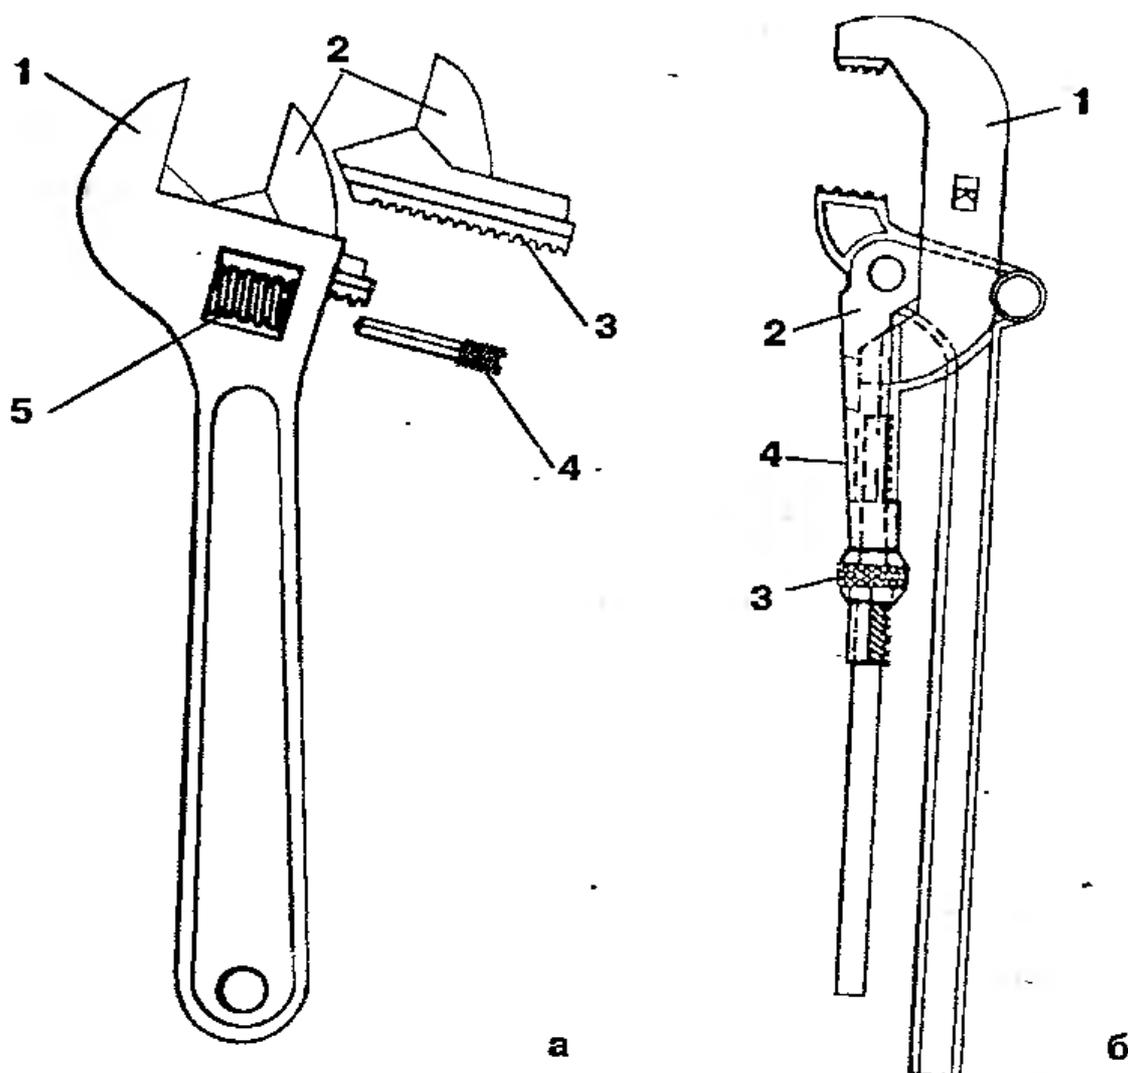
Ключи: а — разводной гаечный (1 — неподвижная губка; 2 — подвижная губка; 3 — рейка; 4 — ось; 5 — червяк); б — трубный рычажный (1 — неподвижный рычаг; 2 — подвижный рычаг; 3 — гайка; 4 — обойма)
